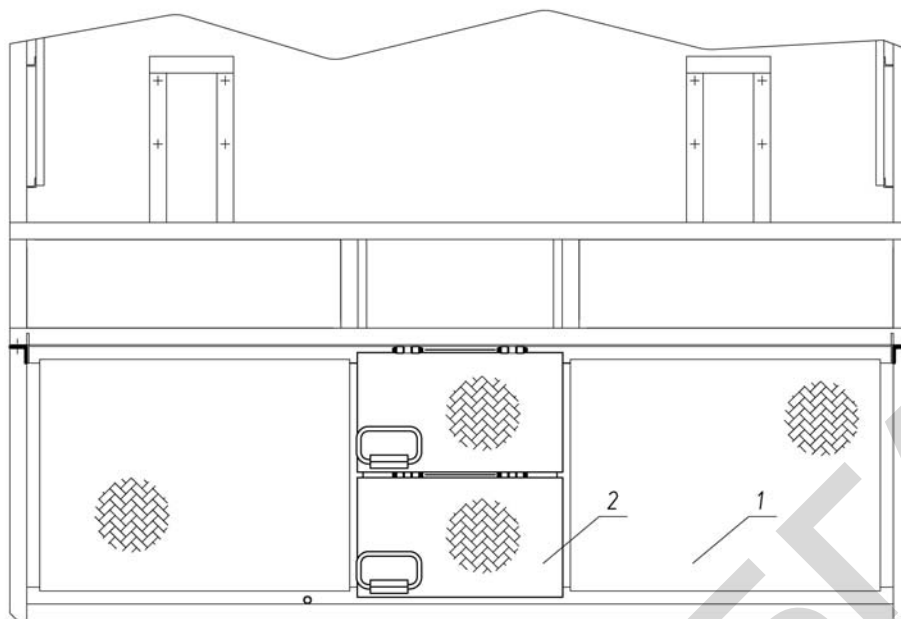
Крышка проема над лестницей: 1 – площадка обслуживания; 2 – крышка
